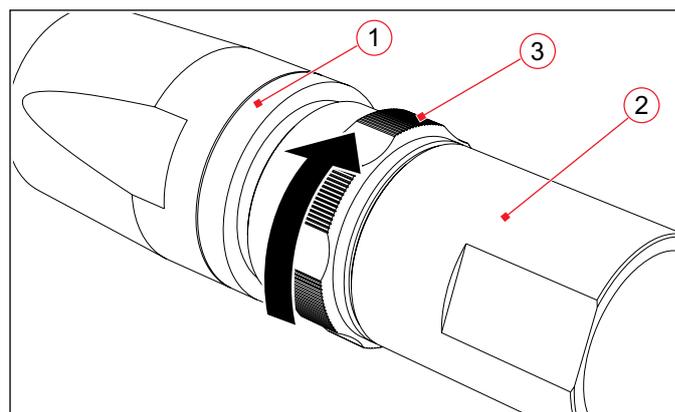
Verschlussring (3) auf Dosengewinde schrauben
